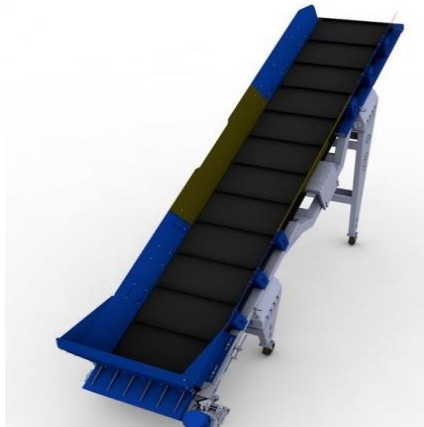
Внешний вид ленточного транспортера с металлодетектором
